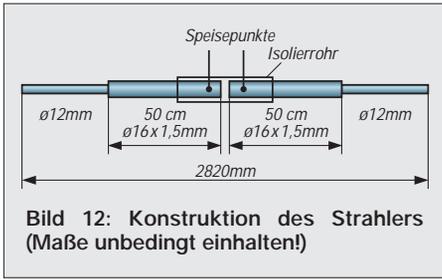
Konstruktion des Strahlers (Maße unbedingt einhalten!)
